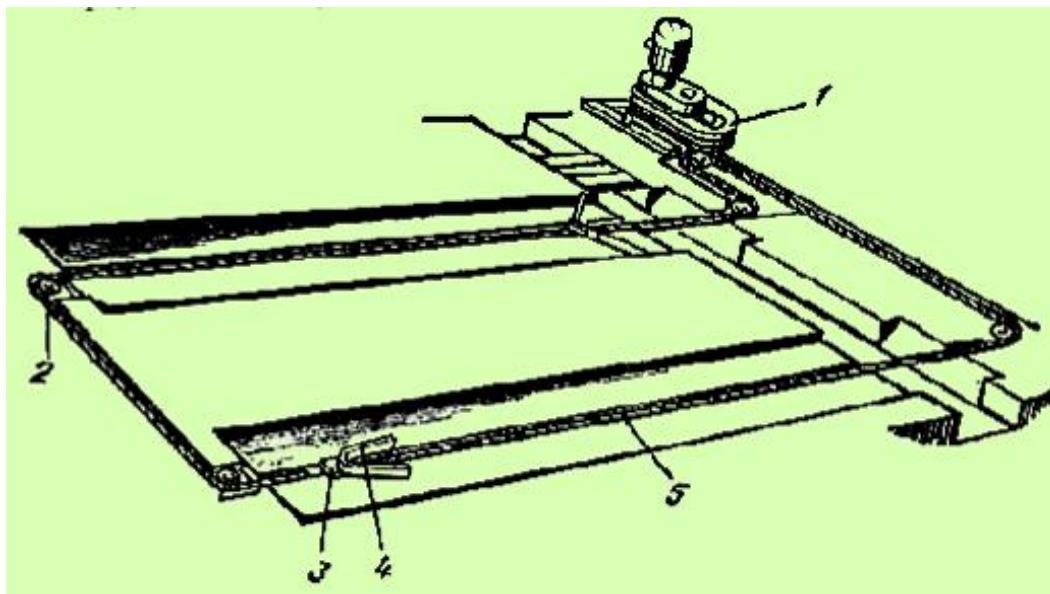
Скреперная установка УС-15: 1 – привод; 2 – поворотное устройство; 3 – ползун; 4 – скребок; 6 – цепь.
